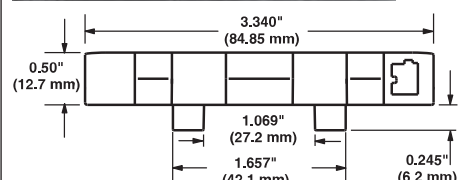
S1400 Flat Top moulé à la largeur 85 mm
